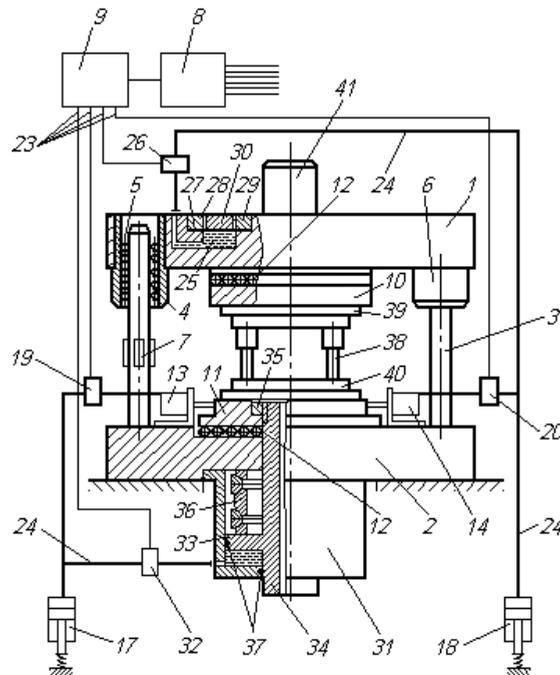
Схема усовершенствованного штамподержателя, обеспечивающего автоподстройку положения штампа относительно ползуна и стола пресса вертикального типа
